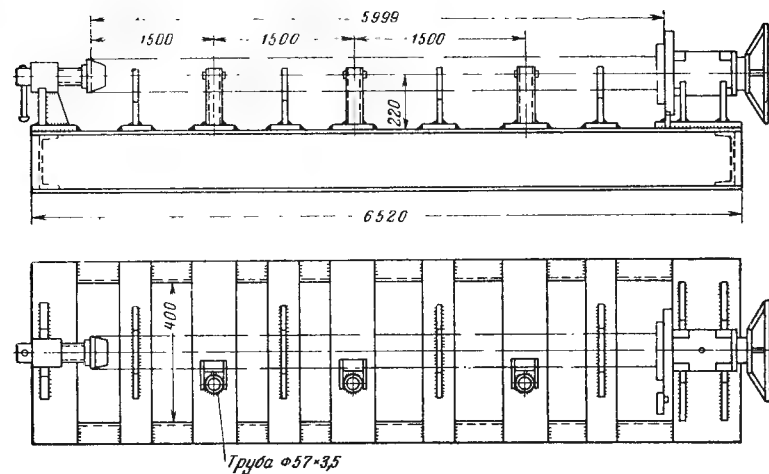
Стенд для предварительной сборки деталей теплообменника «труба в трубе».
